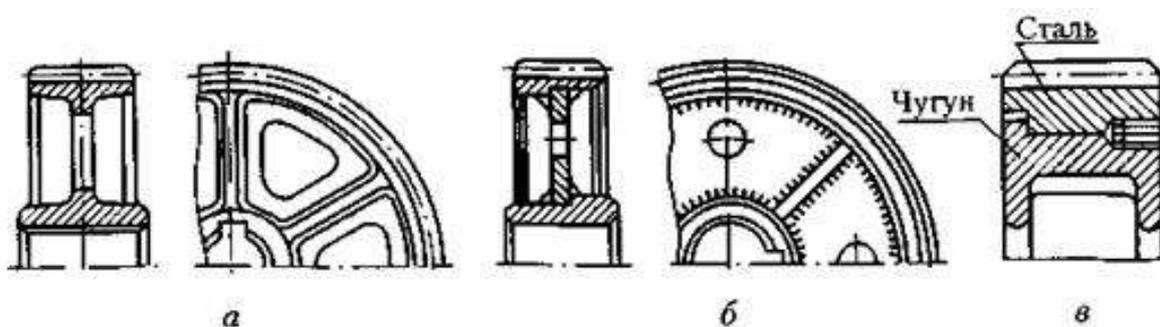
Варианты изготовления зубчатых колес большого диаметром
